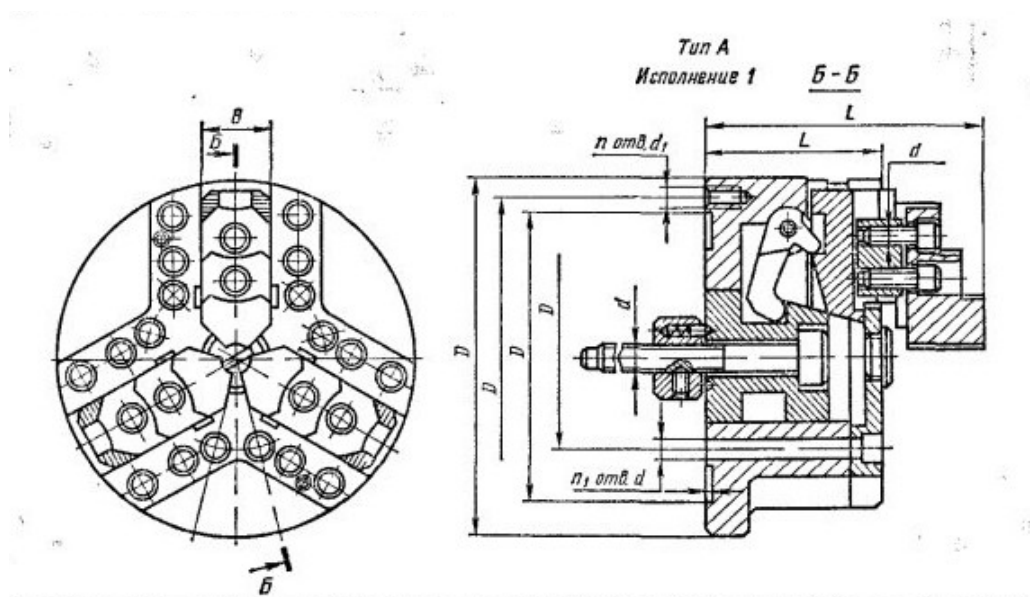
Способ крепления заготовки в зажимном устройстве
